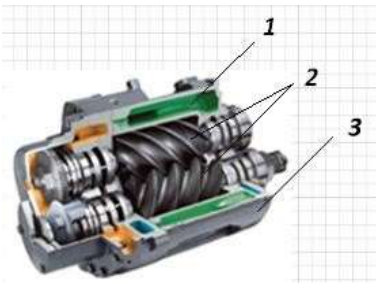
Гвинтовий компресор: 1 – сорочка охолодження; 2 – гвинтова пара; 3 – корпус
